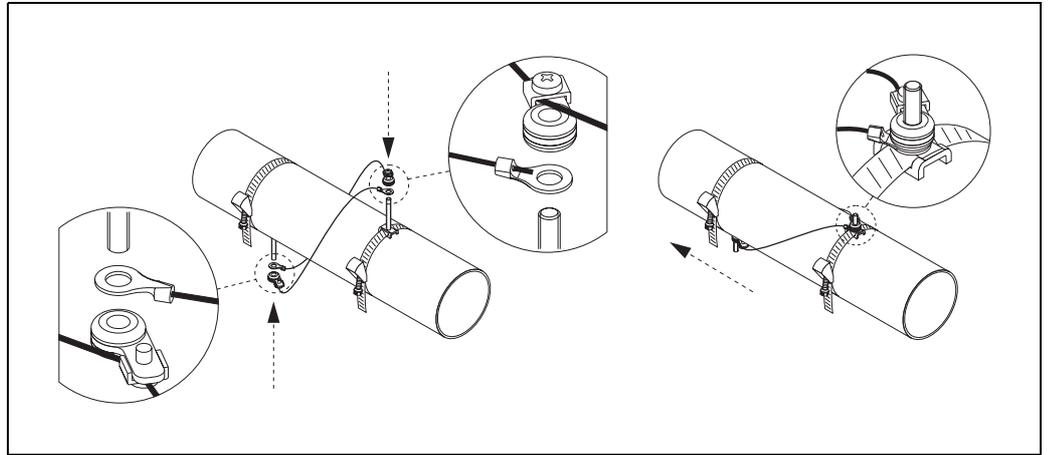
Utilización del dispositivo de medición del cable para el posicionamiento de los pernos roscados
